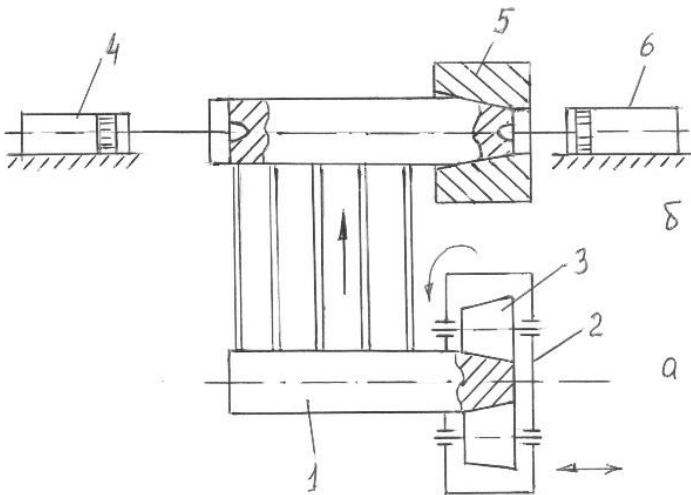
Схематичний вид установки для підготовки заготовки до прошивання: а) перша позиція; б) друга позиція; 1 – заготовка; 2 – обойма; 3 – холості ролики; 4 – гідроциліндр заштовхувача заготовок; 5 – матриця; 6 – гідроциліндр переміщення бойка
